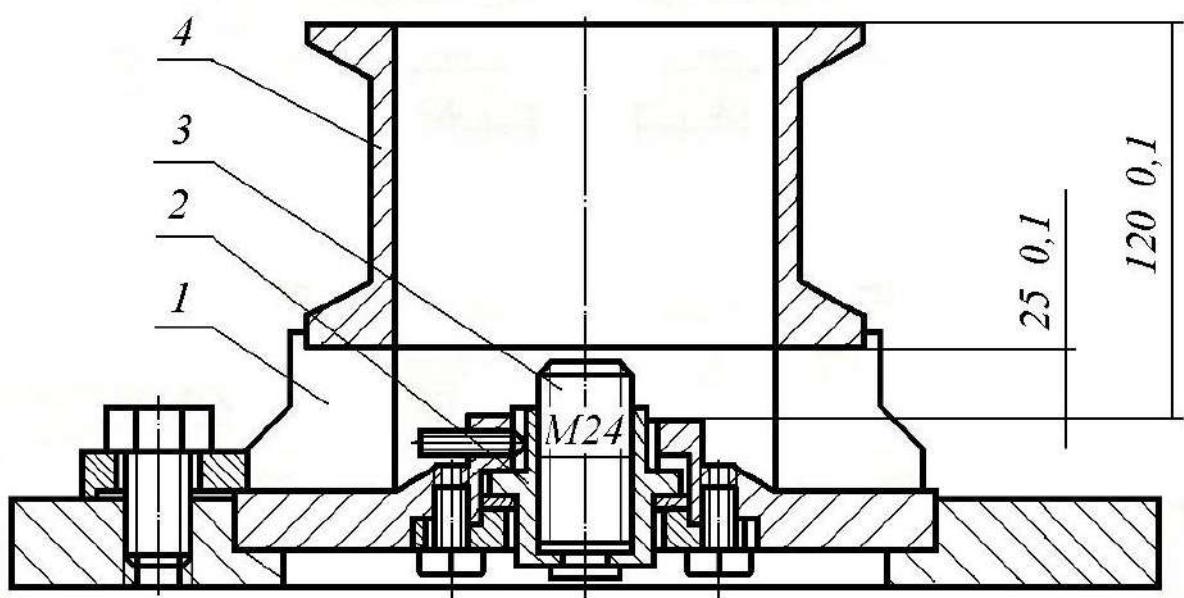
Эскиз опоры для сборки-разборки насоса.
